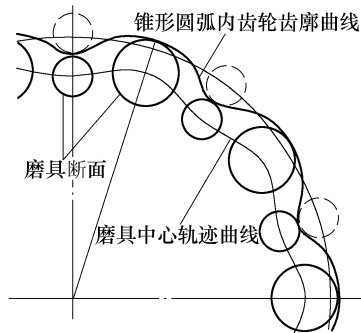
圆弧内齿轮磨削加工磨具中心轨迹
